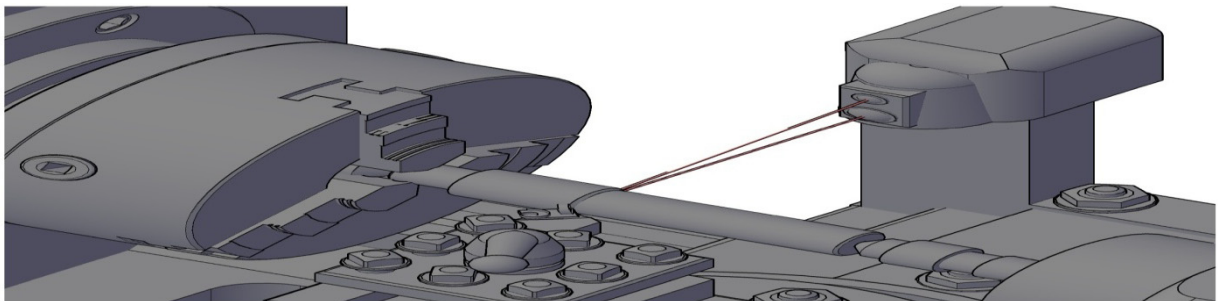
Обработка направляющей колонки с активным лазерным контролем
